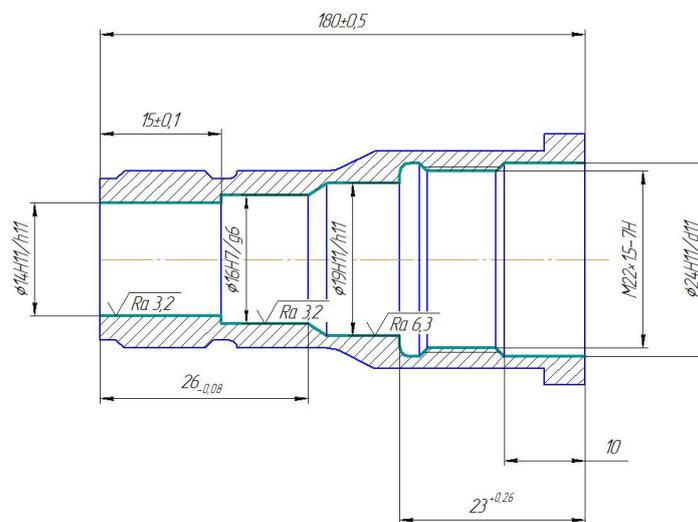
Ответная часть корпуса форсунки BOSH KCA27S55465
